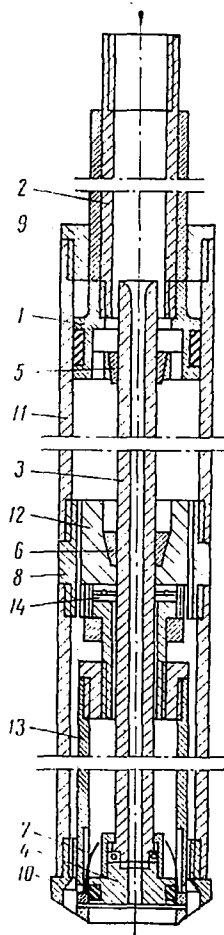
Двойной колонковый снаряд с непрерывным подсосом керна. 1 — поршни; 2 — ведущая труба; 3 — труба; 5, 6 — верхний и нижний подхваты; 7 — кернорвательные пружины; 8, 9 — переходники; 10 — буровая коронка; 11 — цилиндр; 12 — промывочный канал; 13 — керноприемная труба; 14 — подшипник.
